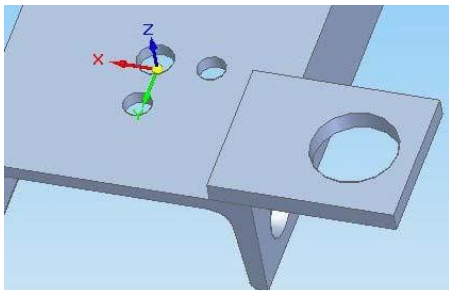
Bohrungen für Rollenaufnahme (Bild 9, Detail 16)
